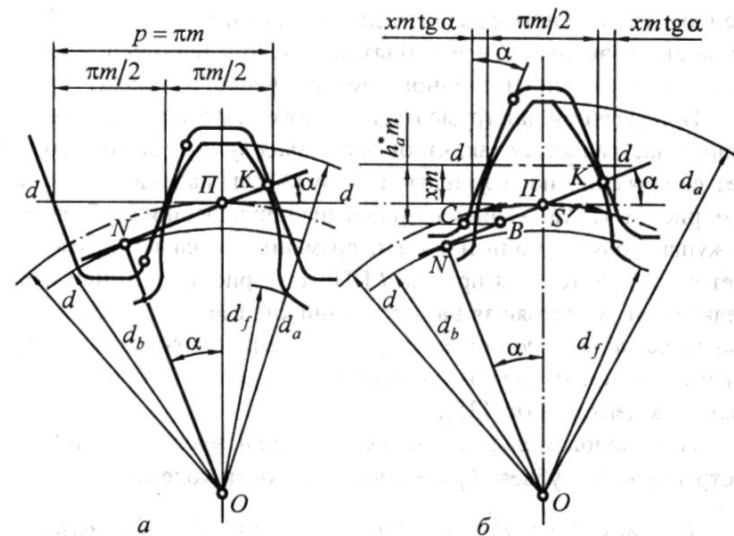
Станочное зацепление реечного инструмента с нарезаемым зубчатым колесом:
